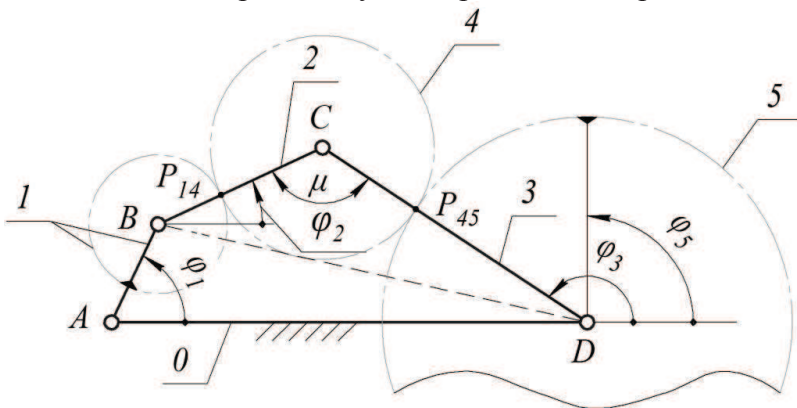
Зубчато-рычажный механизм Роттенбахера
